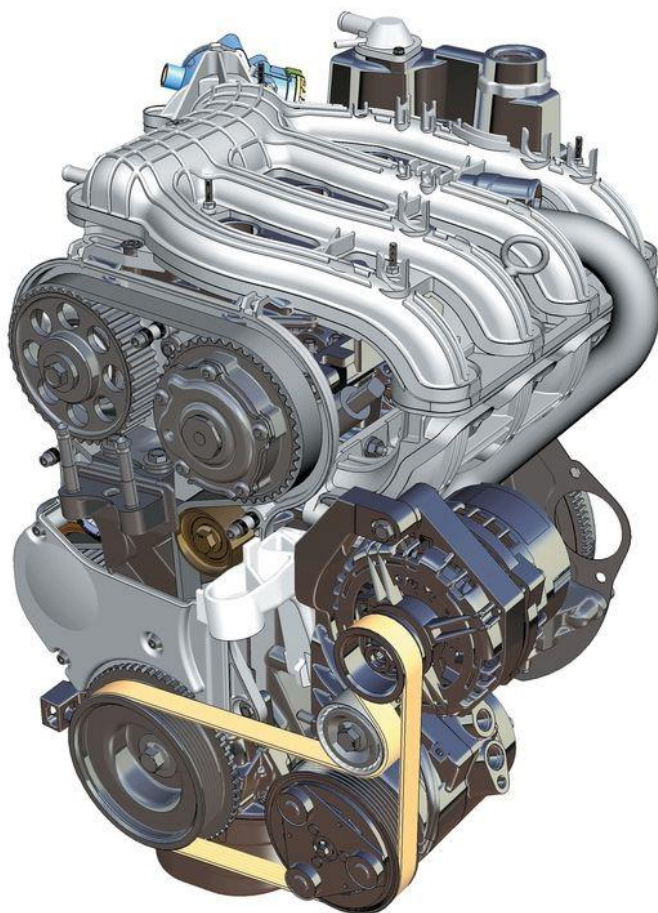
Внешний вид двигателя ВАЗ 21127
